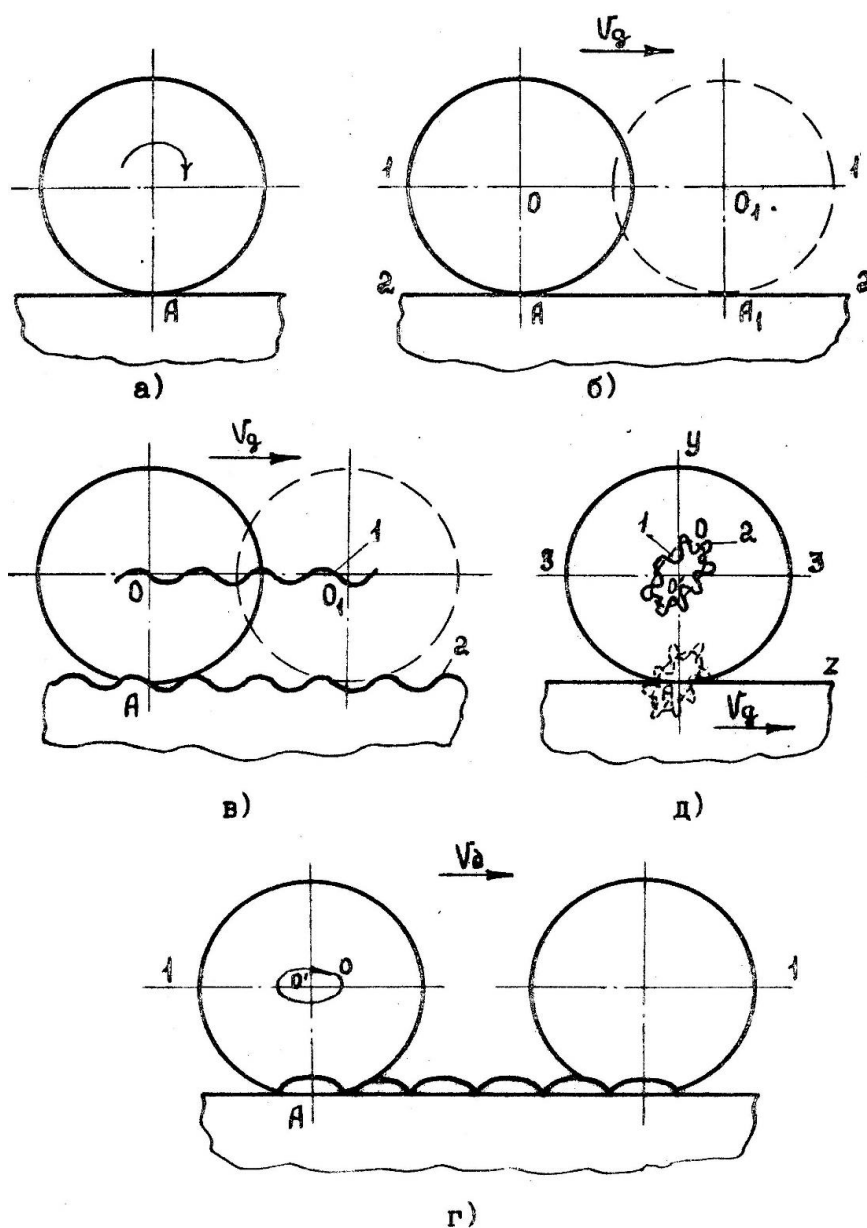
Схема траектории движения формообразующей точки круга и формирование волнистости на обрабатываемой поверхности
